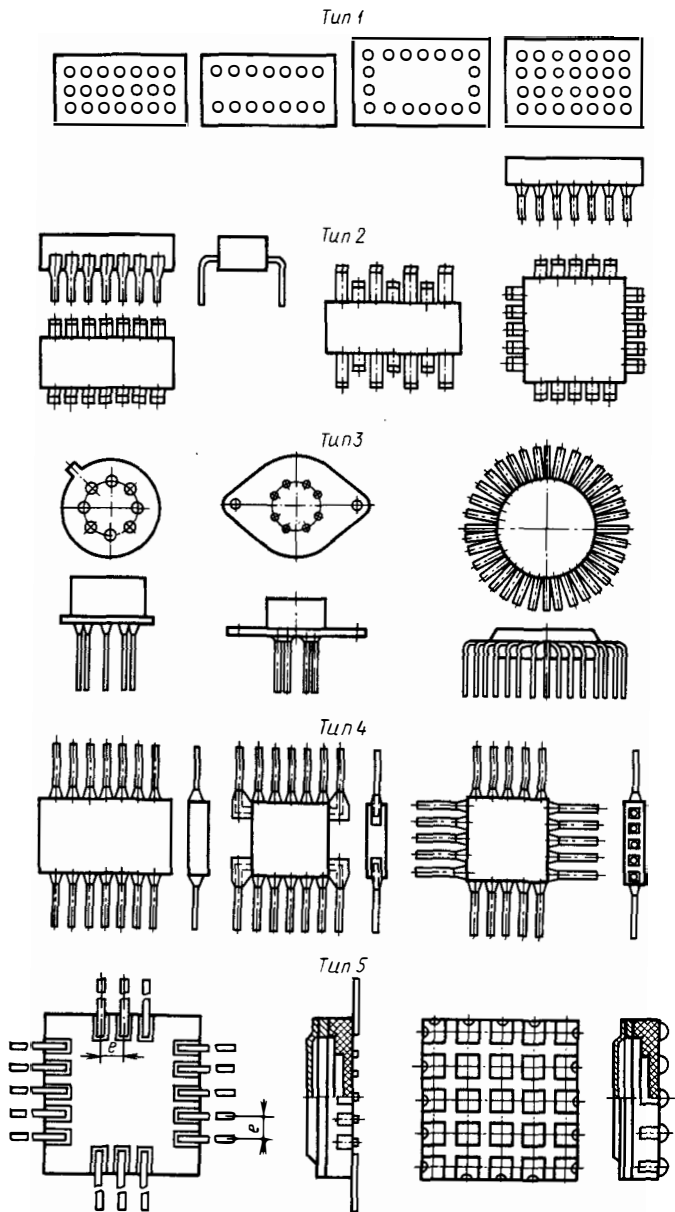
Типы корпусов ИС (e — шаг расположения выводов)
